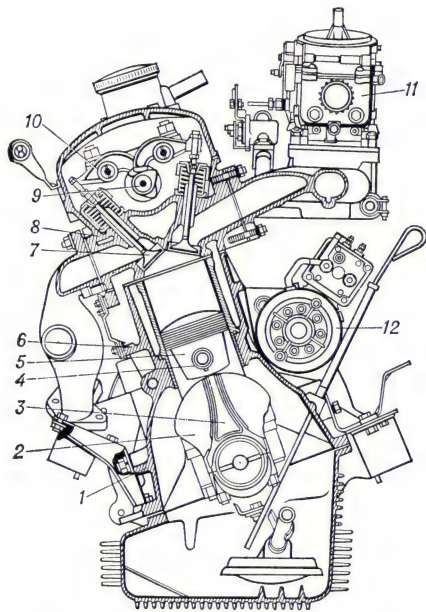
Поперечный разрез карбюраторного двигателя МЗМА-412: 1 — картер; 2 — коленчатый вал; 3 — шатун; 4 — поршневой палец; 5 — поршень; 6 — блок цилиндра; 7 — клапан; 8 — головка цилиндра; 9 — распределительный вал; 10 — коромысло; 11 — карбюратор; 12 — стартер.
